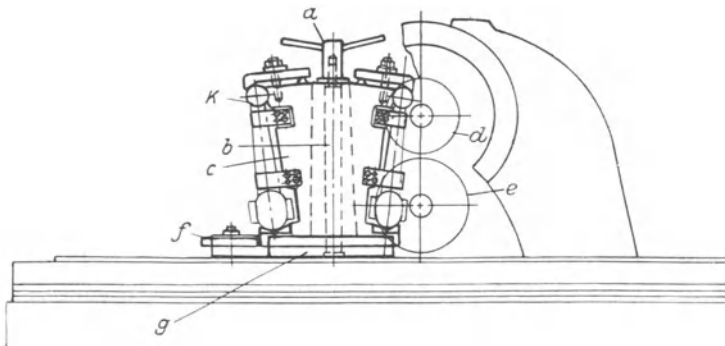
Horizontale Schwenkvorrichtung für Kurbelstangen.
